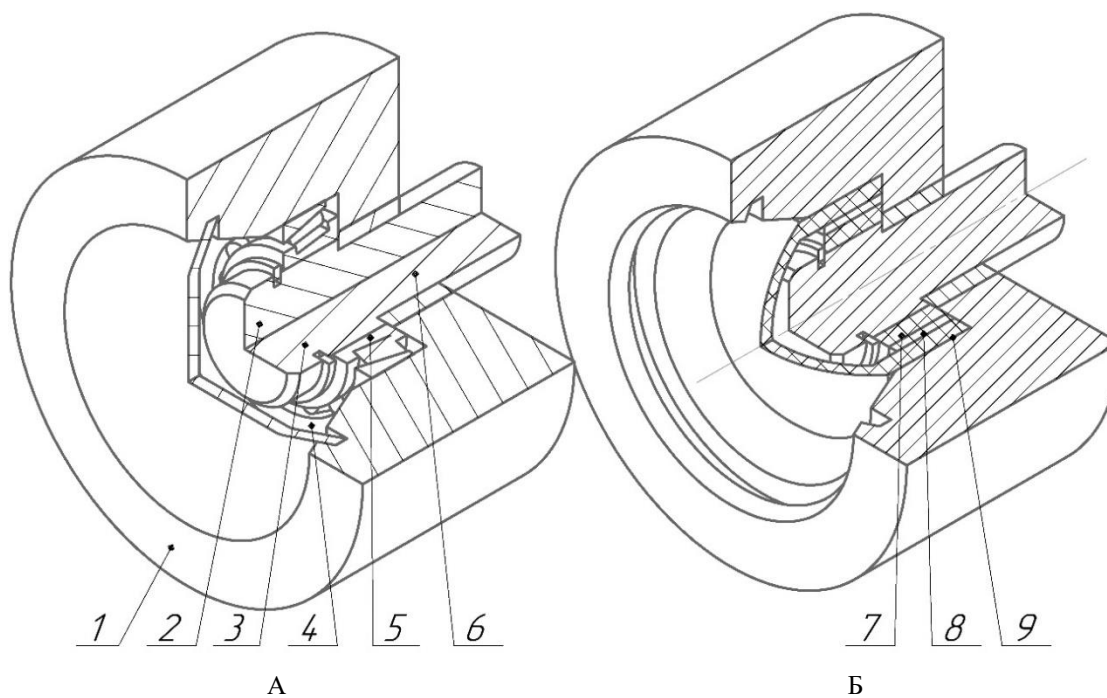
Базовая (А) и модернизированная (Б) конструкции подшипникового узла поддерживающего ролика элеватора
